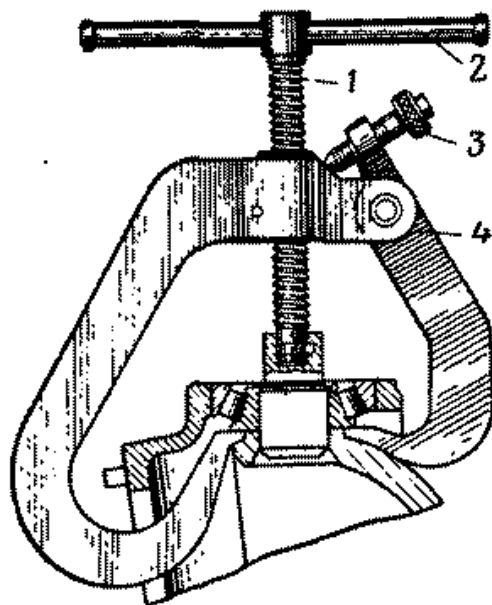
Снятие подшипника шкворня поворотного кулака шаровой опоры:
